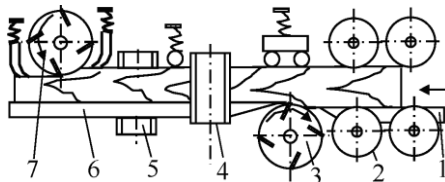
Схеми чотирибічного поздовжньо-фрезерного верстата
